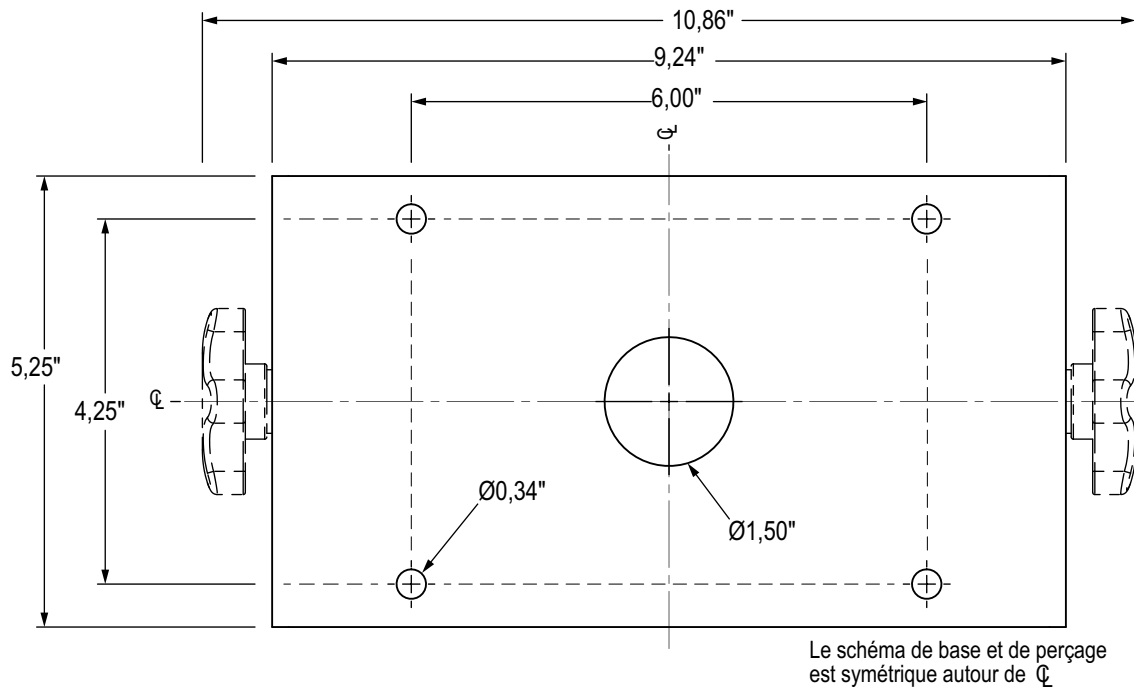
Configuration cotée des perçages du support inclinable pour modèle universel
